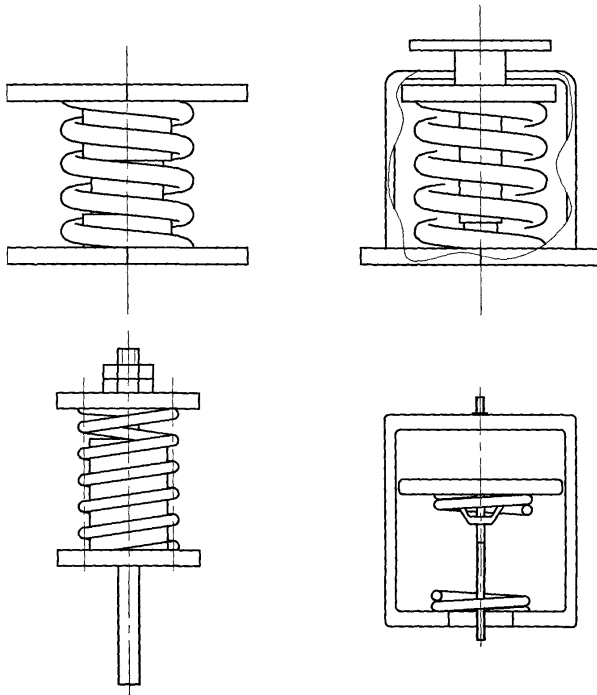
Примеры исполнений пружинных блоков (с корпусом и без корпуса)
